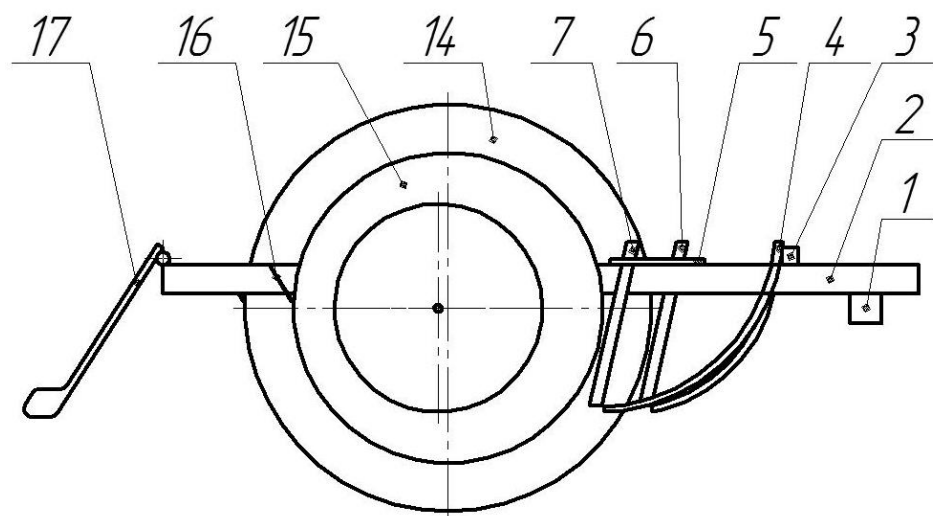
Конструкторско-технологическая схема сошника зернуковой сеялки (вид сбоку)
